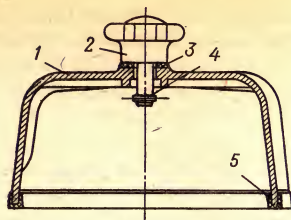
Крышка головки цилиндров двигателя ЯМЗ-240Б:
